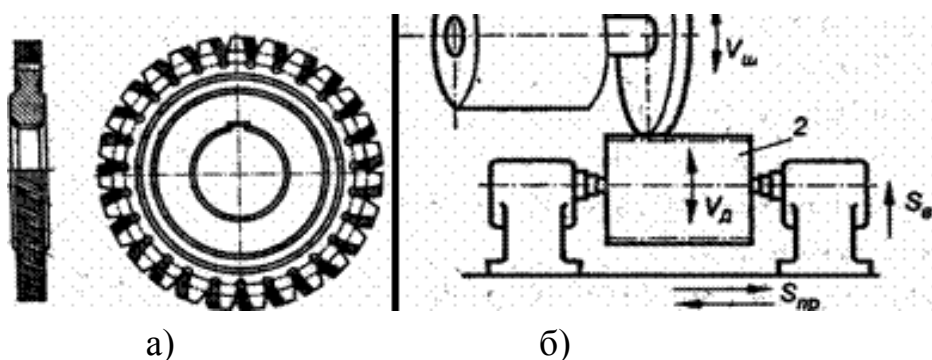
Шевингование: а – дисковый шевер; б – схема обработки зубьев колес дисковым шевером
